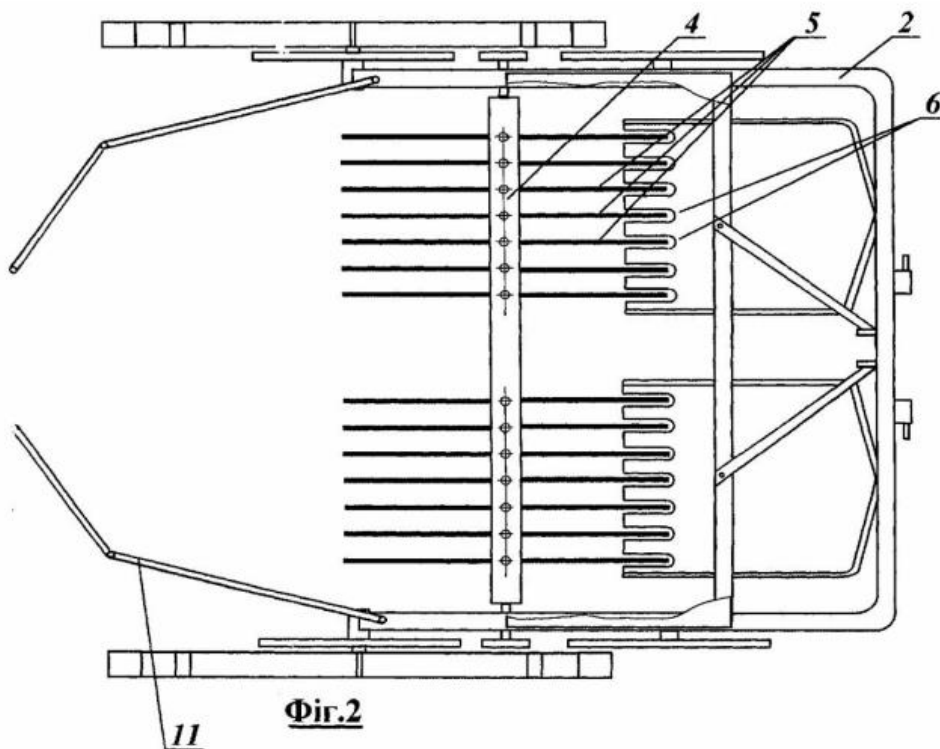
Роторний копач коренеплодів (вид зверху)
